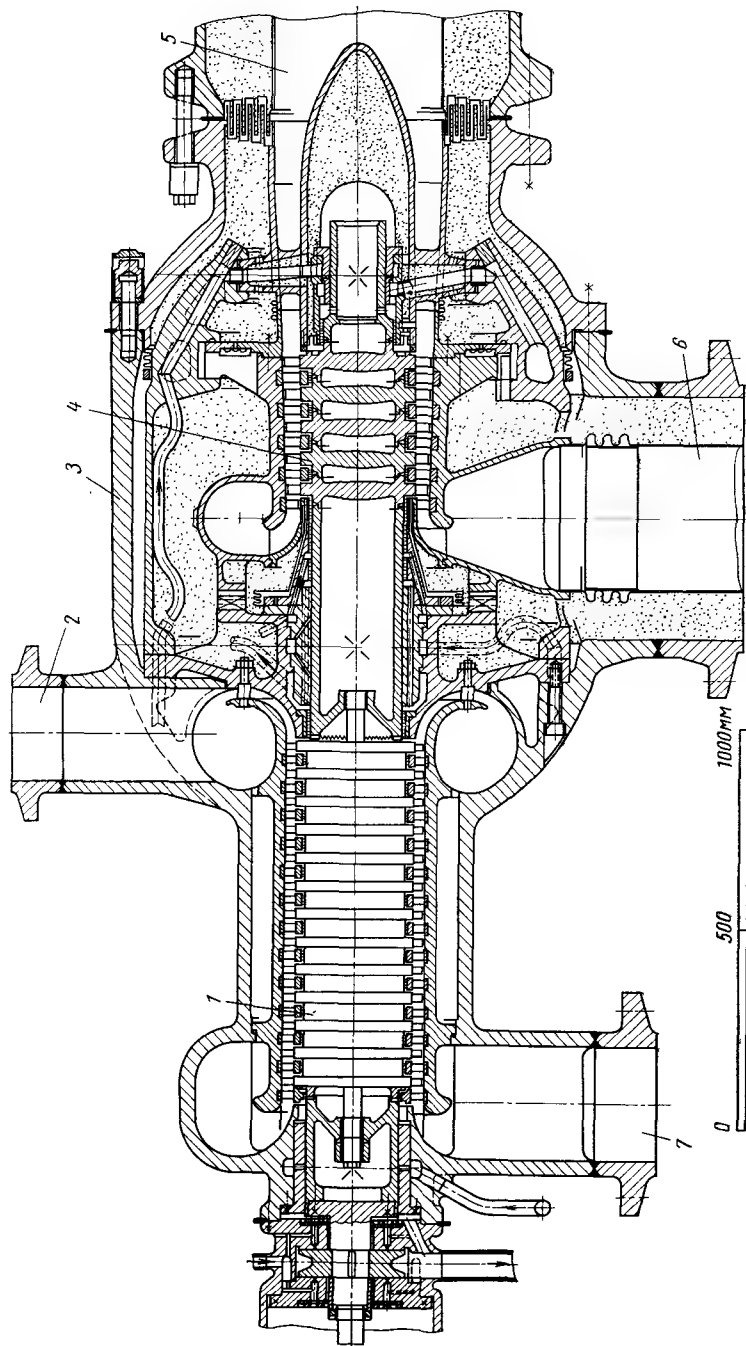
Продольный разрез ГТУ замкнутого цикла фирмы Швер — Висс мощностью 10000 л. с. для судовой установки (только турбокомпрессор без силовой турбины): 1 — компрессор; 2 — выпускной патрубком компрессора; 3 — корпус турбокомпрессора; 4 — корпус турбины; 5 — входной патрубок турбины; 6 — входной патрубок компрессора; 7 — выпускной патрубок
